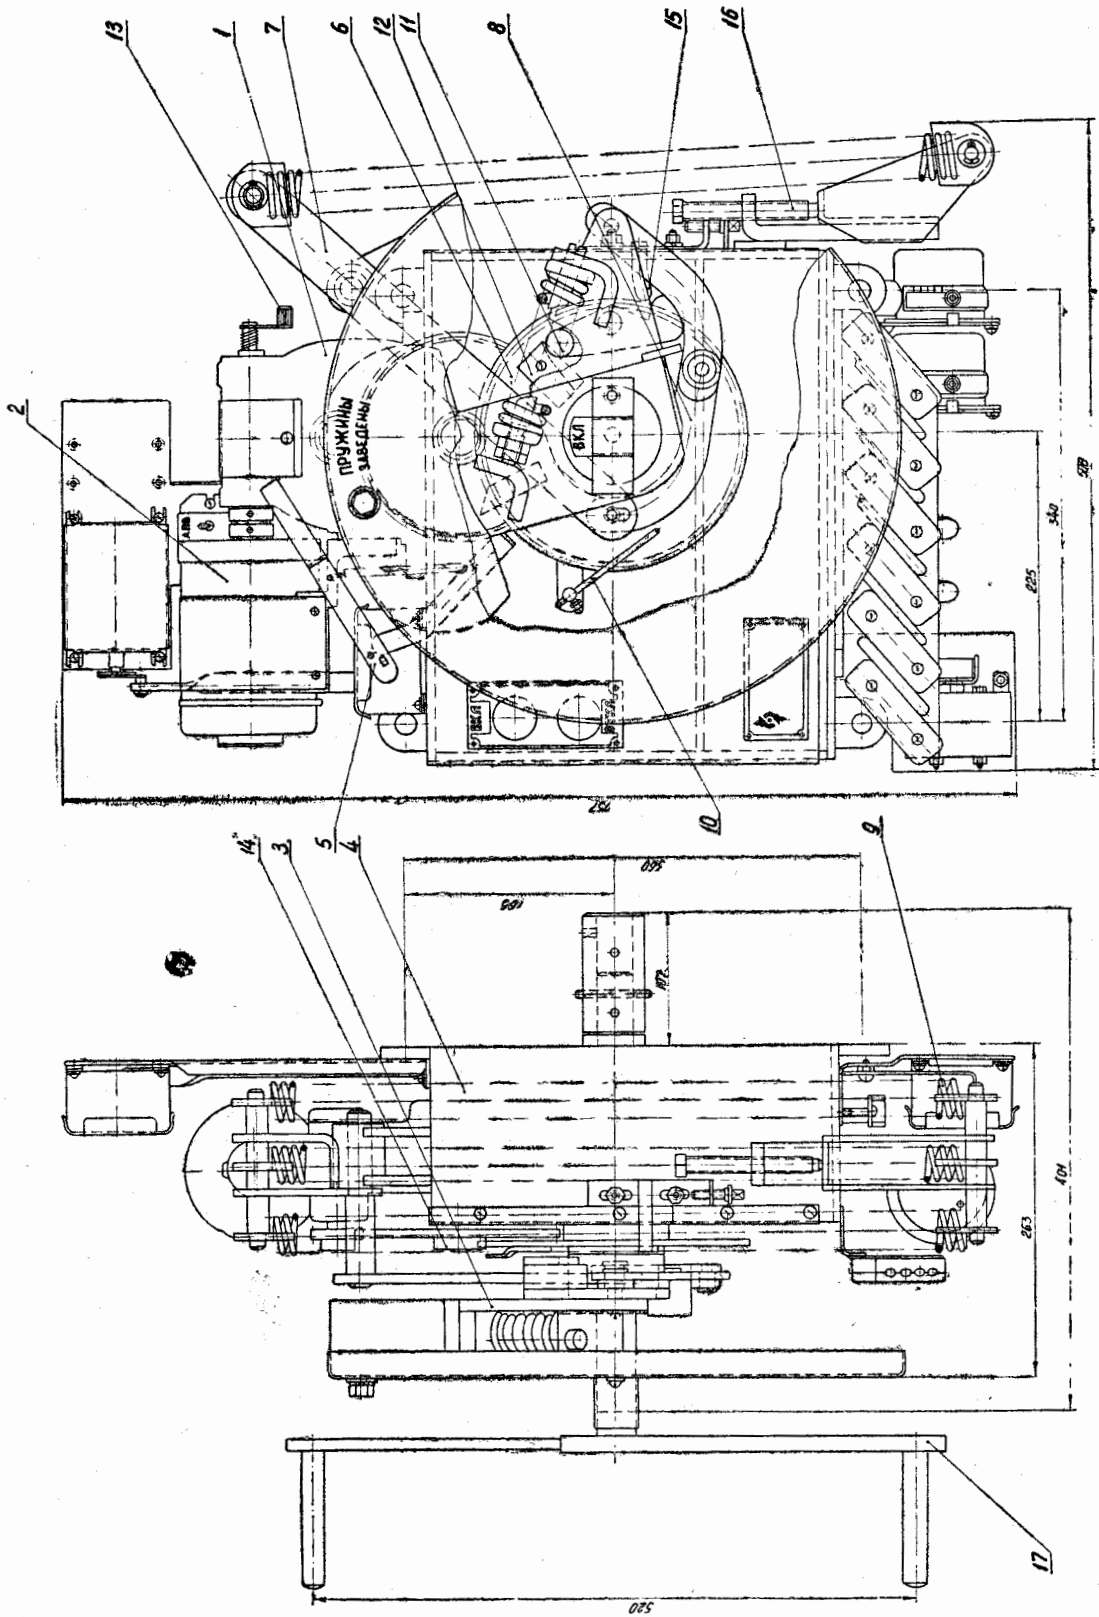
Общий вид и габаритные размеры привода ПП-61.
